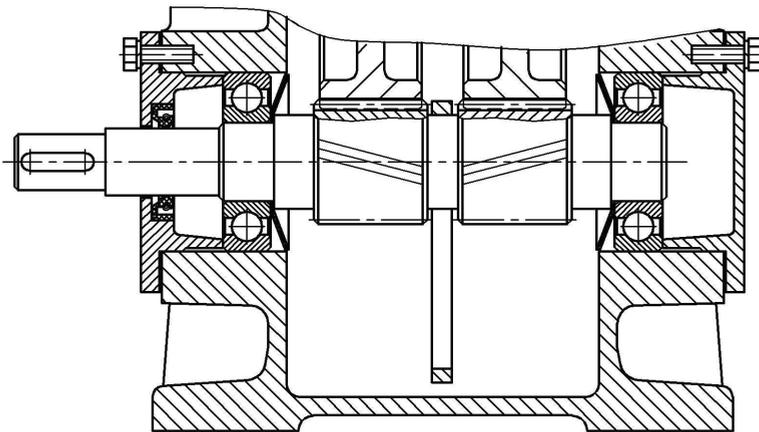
Смазывание колес и подшипников при помощи кольца
